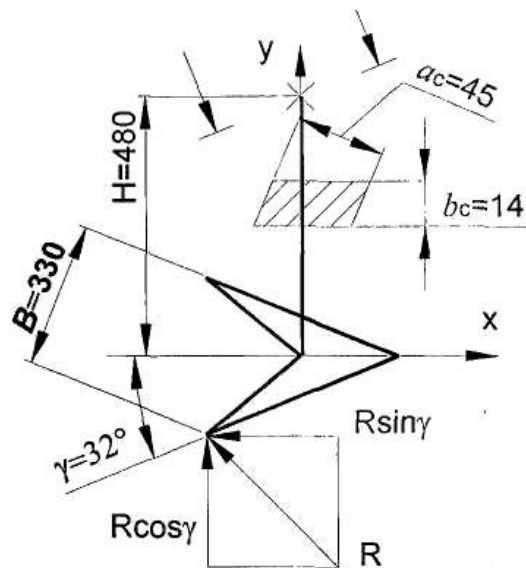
Розрахункова схема стойки культиваторної лапи
